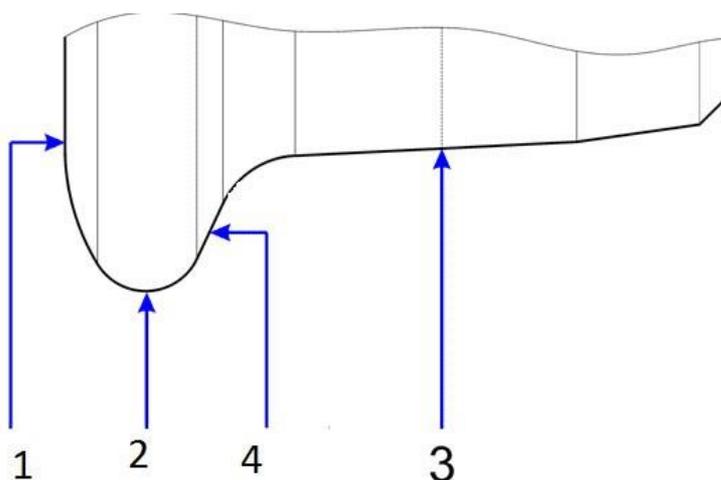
Контролируемые точки профиля обрабатываемого колеса
